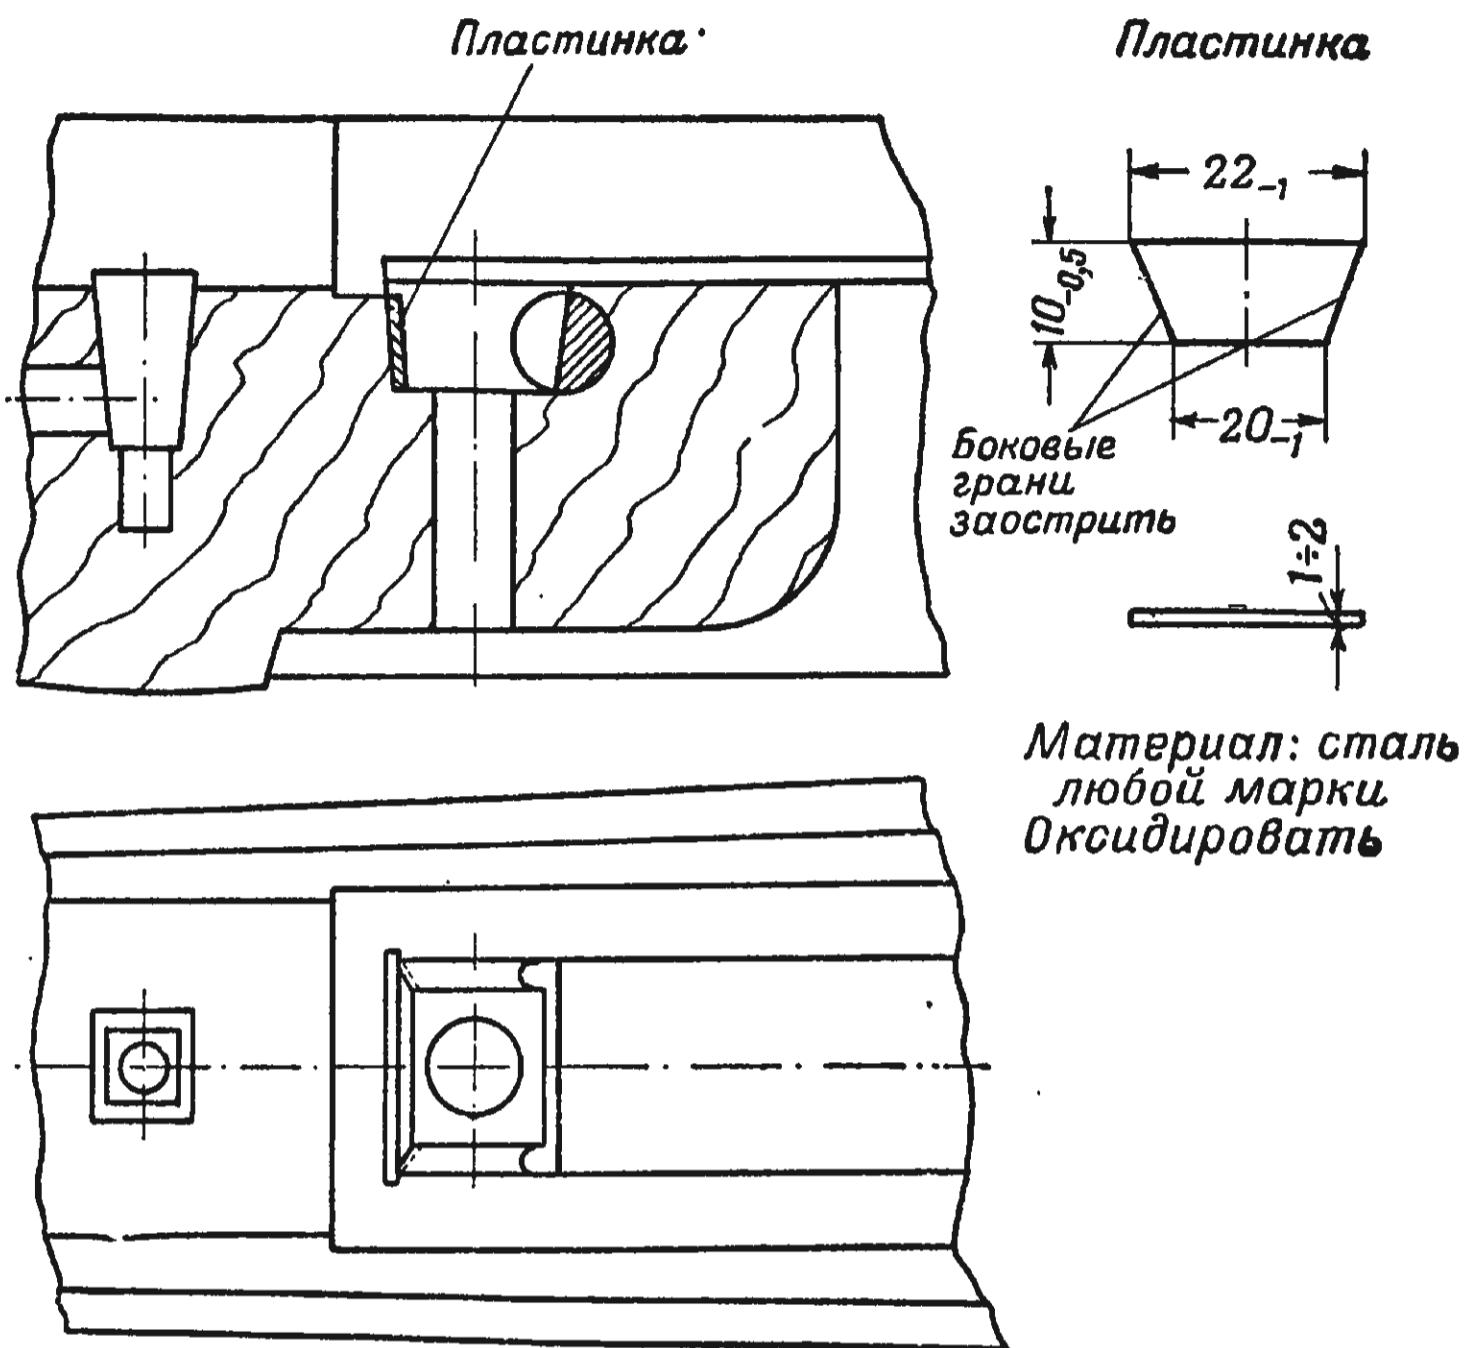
Постановка пластиинки в гнездо ложи для упора ствольной коробки
